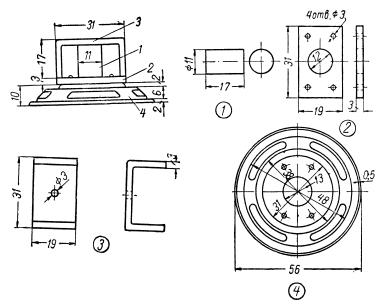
Устройство громкоговорителя с керновым магнитом. *I*—керновый магнит; 2—фланец; 3—скоба; 4—диффузородержатель.
